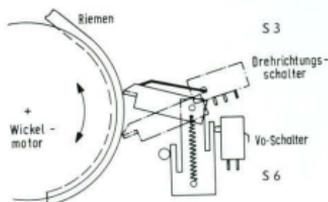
Drehrichtungsabhängiger Vor-Rücklauf-Umschalter
